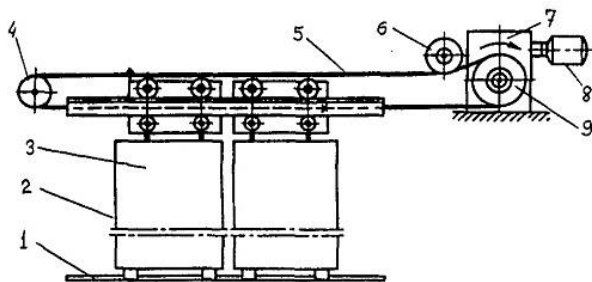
Схема механизма с зубчатой ременной передачей:
